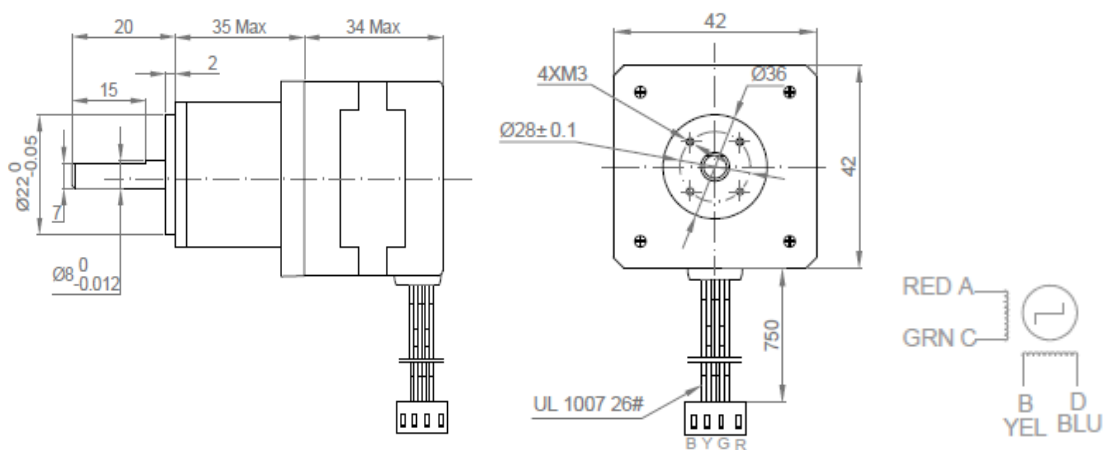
Dimensiones del motor a pasos en mm y configuración de bobinas (motor a pasos bipolar)
